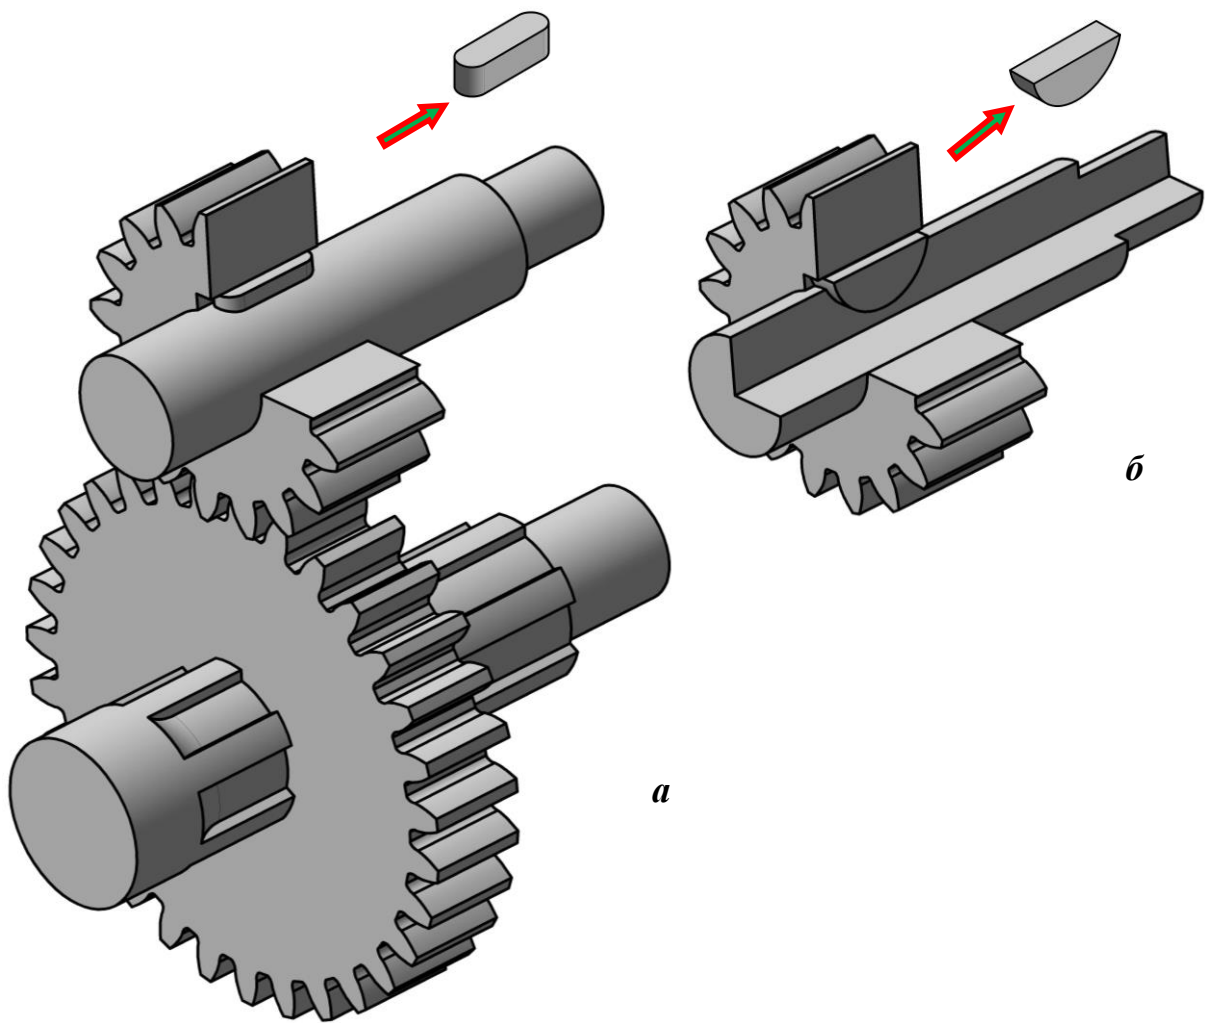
Варианты конструкций для *соединения* зубчатых колес с несущими их валами: *а* – соединение шестерни с валом призматической шпонкой, а большого зубчатого колеса с валом – посредством шлицев; *б* – соединение шестерни с валом сегментной шпонкой
